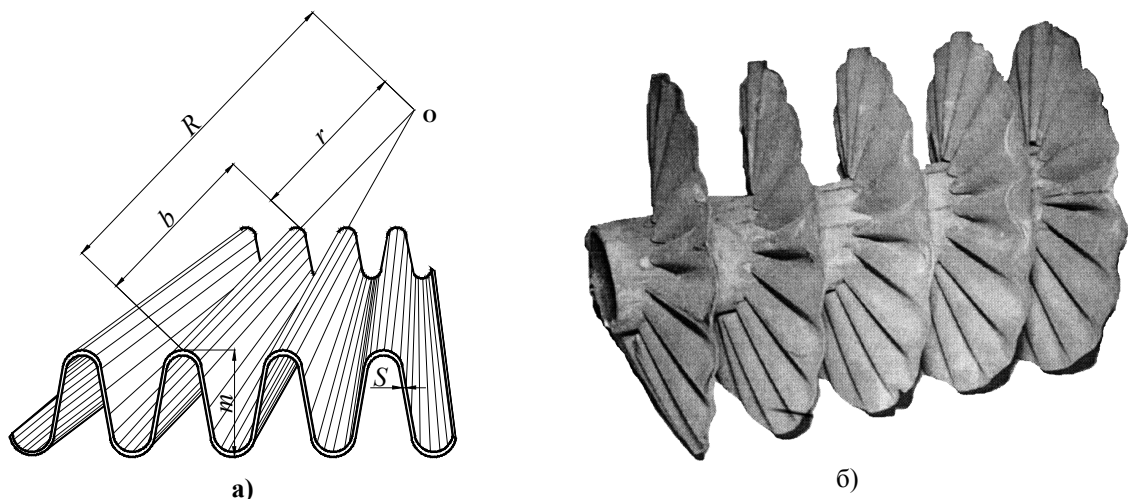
Гвинтова гофрована заготовка: а) параметри гвинтової поверхні; б) шнек з гофрованою гвинтовою спіраллю.
